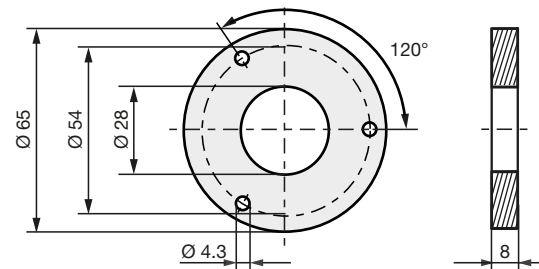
Accesorios especiales BTL-P-1028-15R
